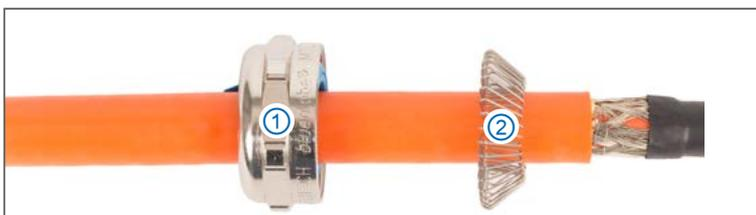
Druckschraube der PG Verschraubung und Federring auf HV-Stromkabel aufziehen.
